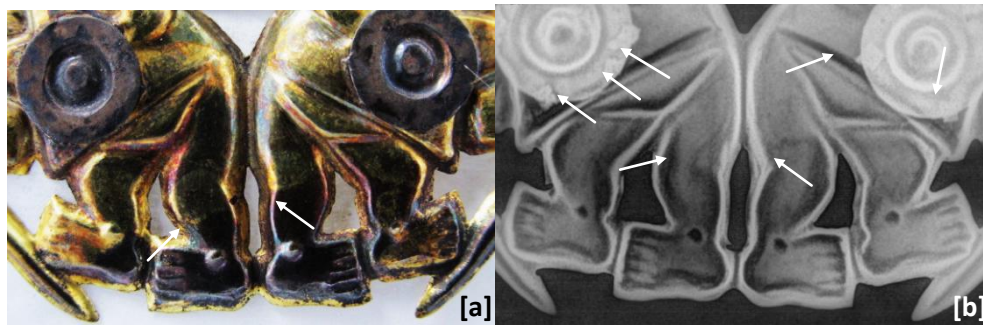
Imagens [a] fotográfica e [b] radiográfica da peça decorativa PD01, com filtro de aumento de detalhes. Pela radiografia é observada a presença de um material intermediário para a soldagem do escudo de sobre soldas os soldados de ouro e uma área pouco escuras nos pés.
